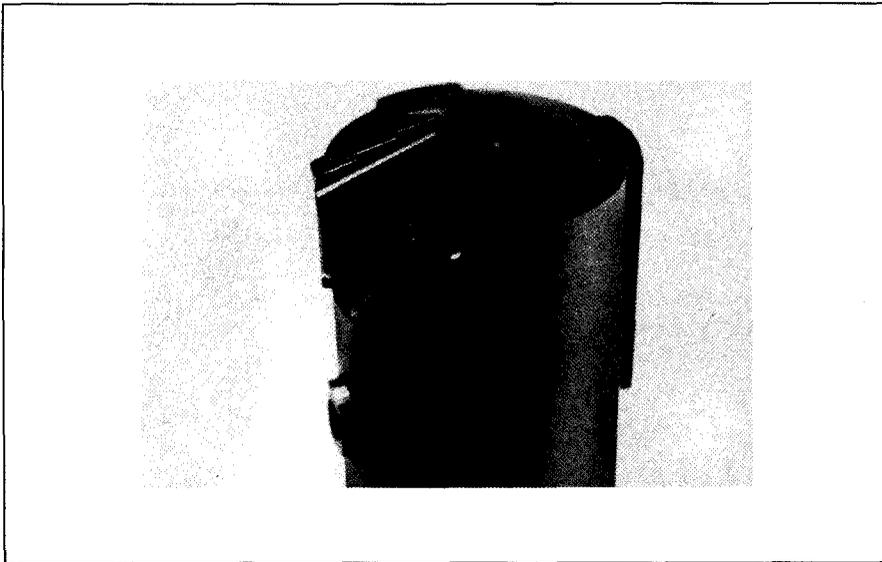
Tieflochbohrwerkzeug mit Wendeschneidplatte (BTA)
